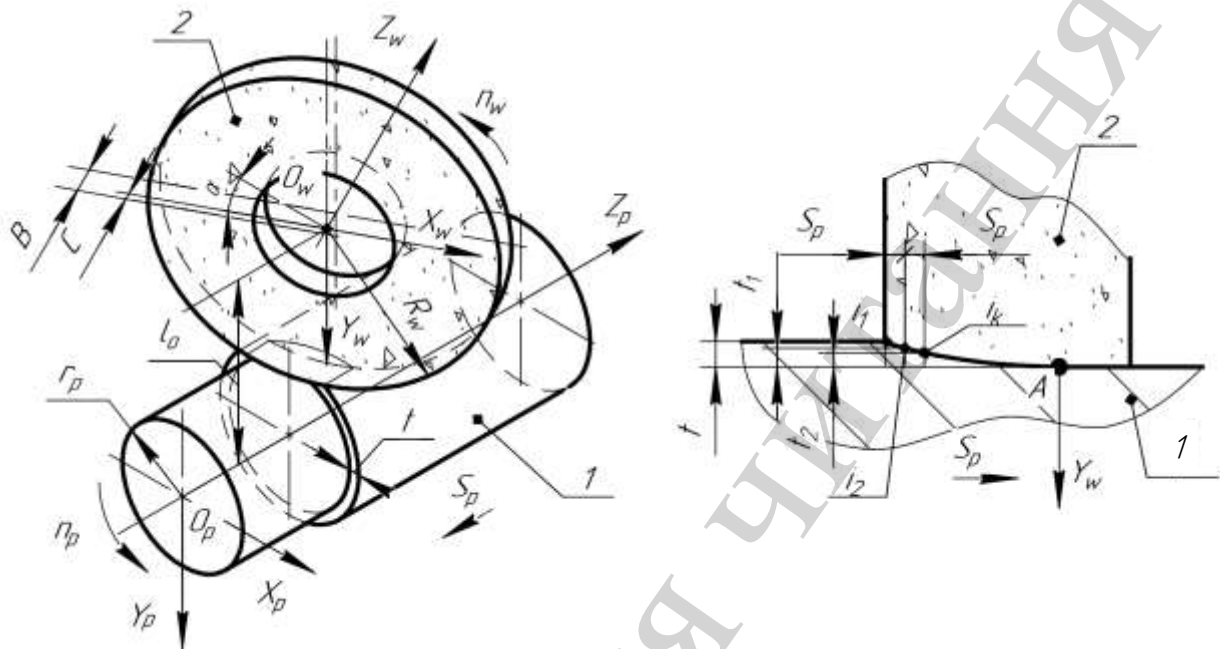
Шліфування циліндричного вала периферією орієнтованого інструмента
